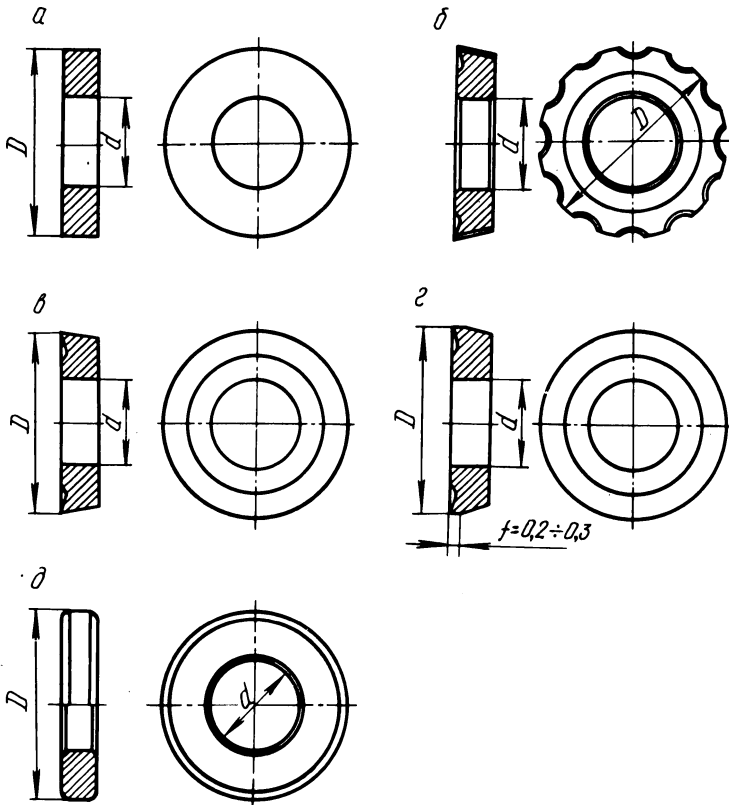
Заготовка и твердосплавные зубья-кольца.
